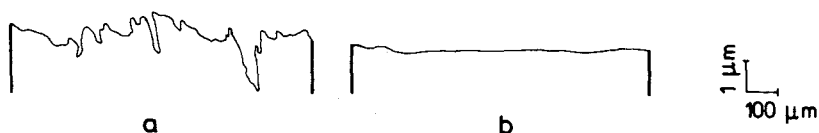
Oberflächenprofilkurven von a) feingeschliffenen, b) hochglanzpolierten Stahlflächen (nach /5/)
